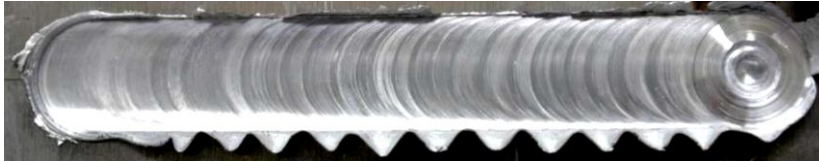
Soldadura con rebaba continua – 1750rpm a 1mm/seg.
